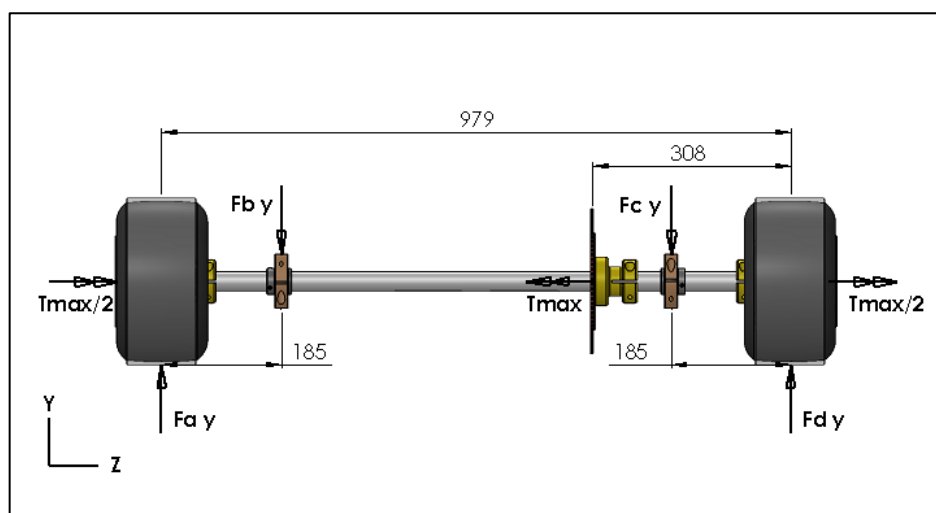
Distribuição das forças no plano horizontal (YZ)
